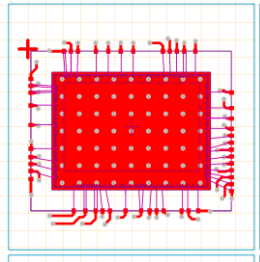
Design der Bildsensor-Montagefläche.
